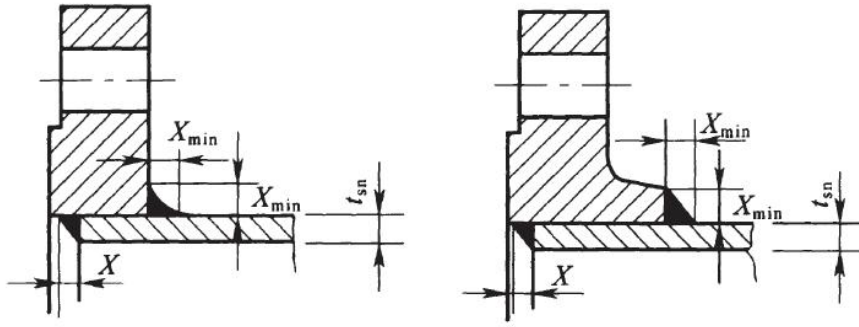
平焊(滑套)法兰内侧和外侧焊缝
